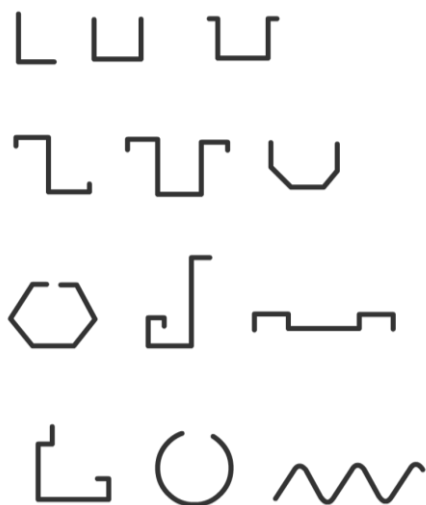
Příklad součástí vyrobených v ohýbadlech
